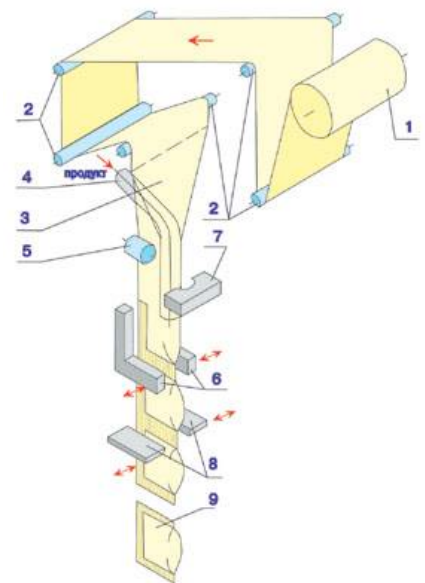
Компонування машини L-подібними зварними губками: 1 – рулон плівки; 2 – направляючі валки; 3 – плівка; 4 – рукавотворювач; 5 – механізм протягування плівки; 6 – губки поперечного зварювання; 8 – відразні ножі; 9 – готовий пакет
